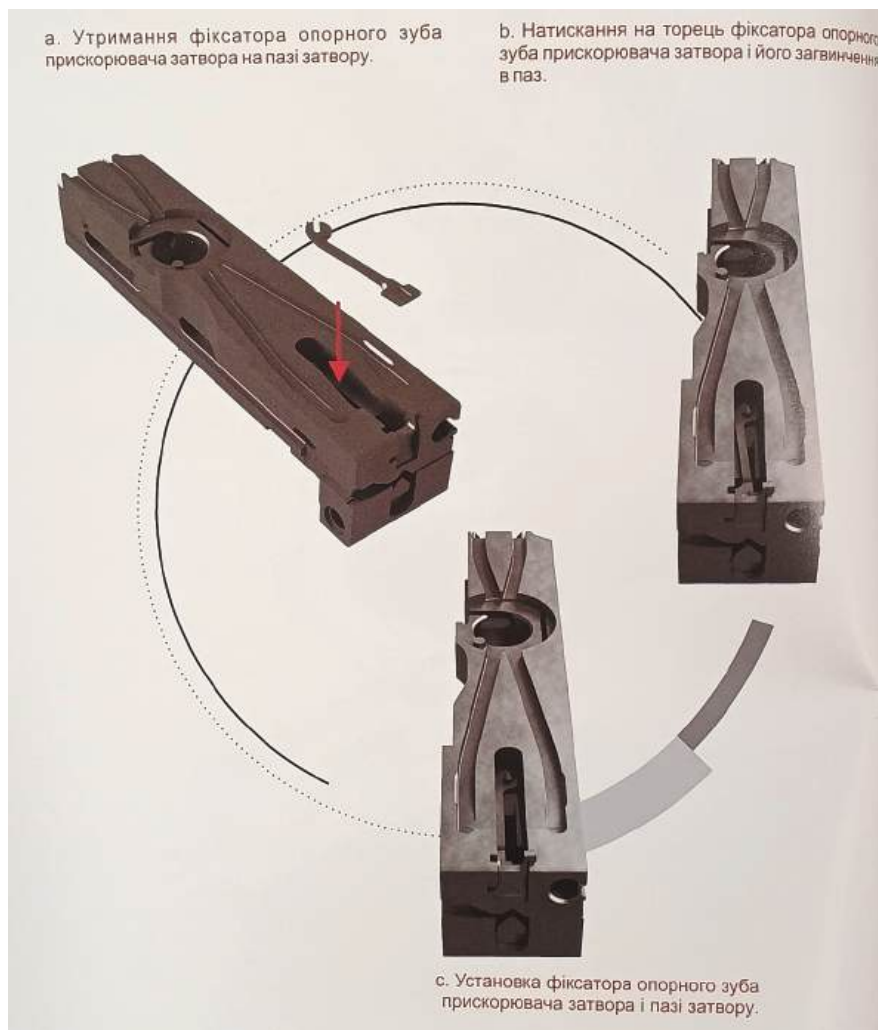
Установка фіксатора опорного зуба прискорювача затвора і пазі затвора
